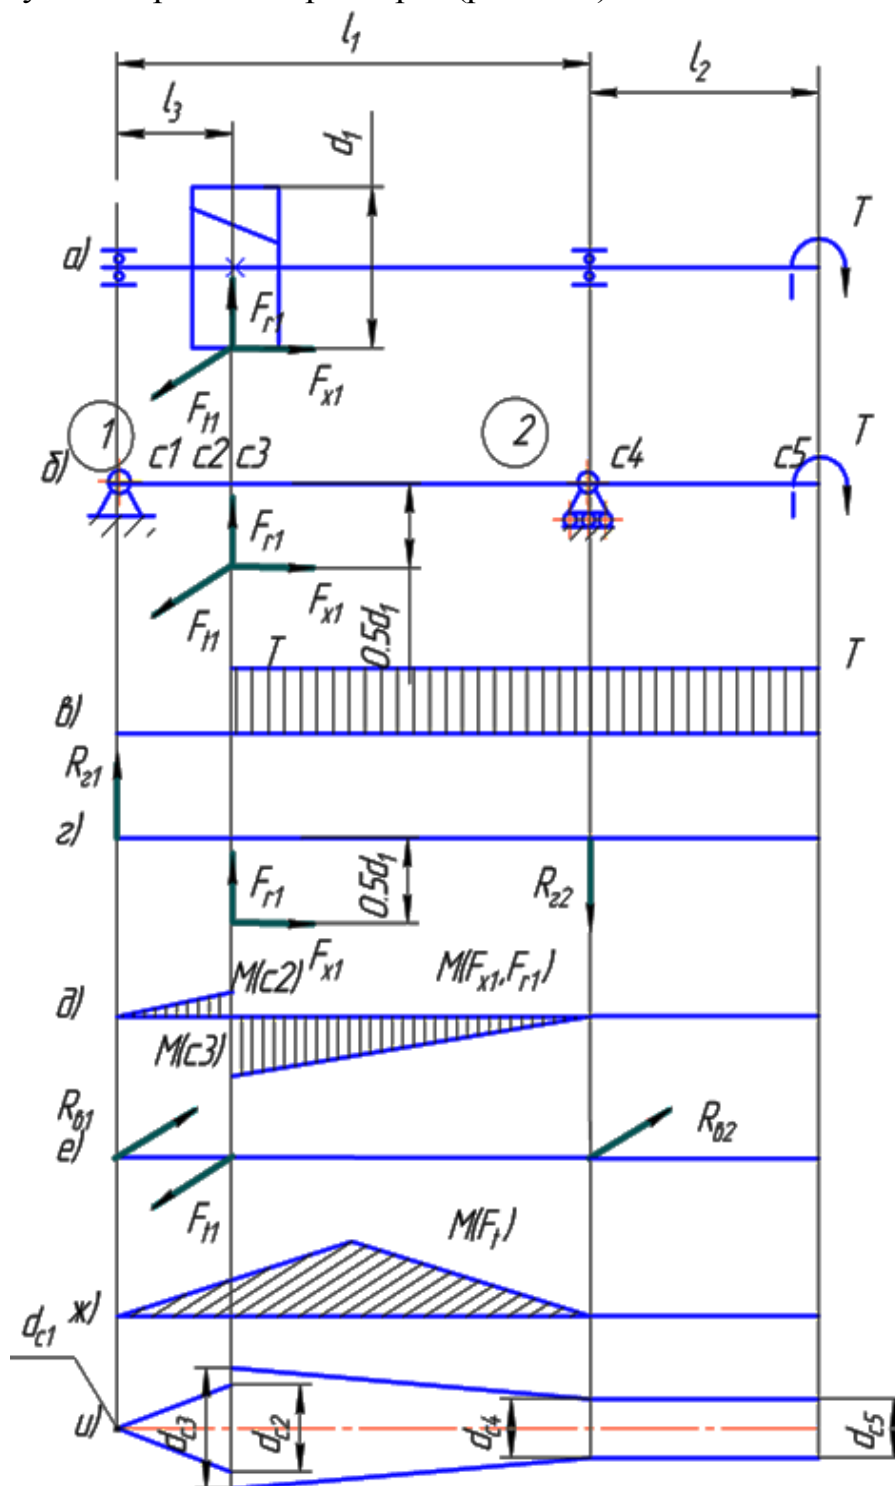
Эпюры вращающего и изгибающих моментов и теоретический профиль ведущего вала редуктора.
